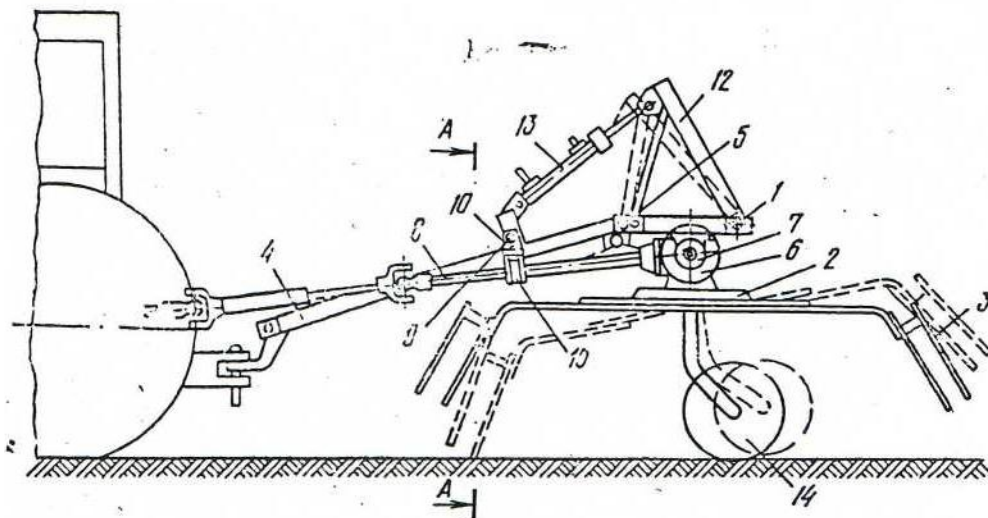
Схема ворушилки [19], вид збоку
